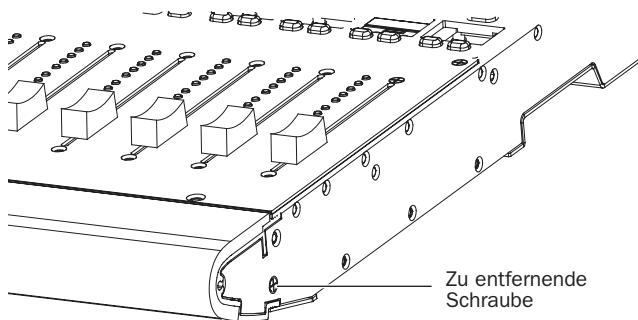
Entfernen der Maschinenschraube von einer Geräteeinheit
